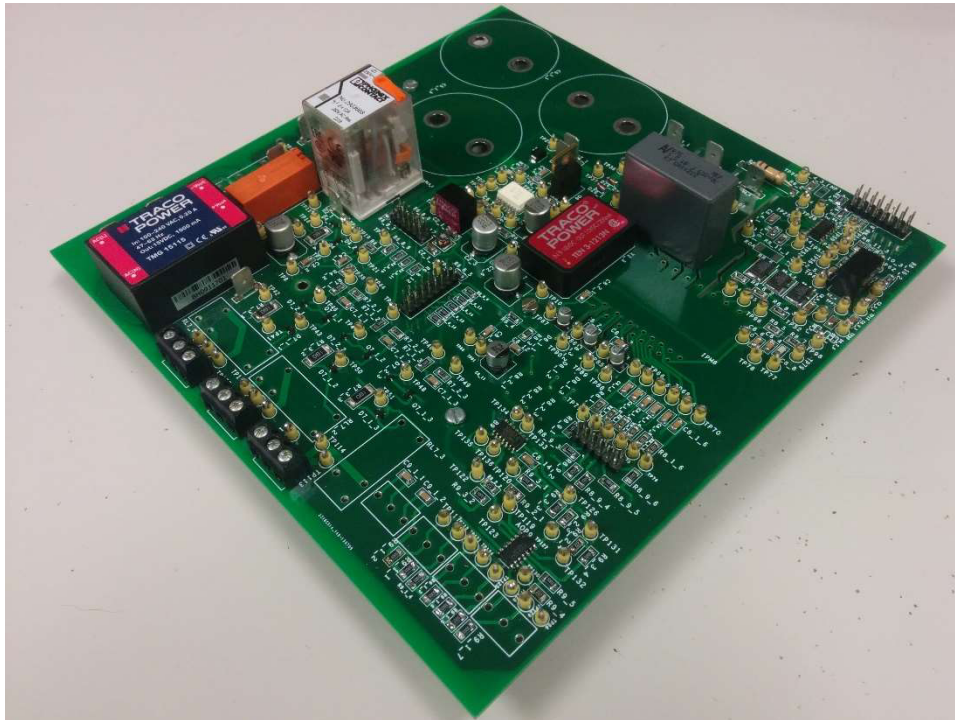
Secuencia de soldadura llevada a cabo en el prototipo
